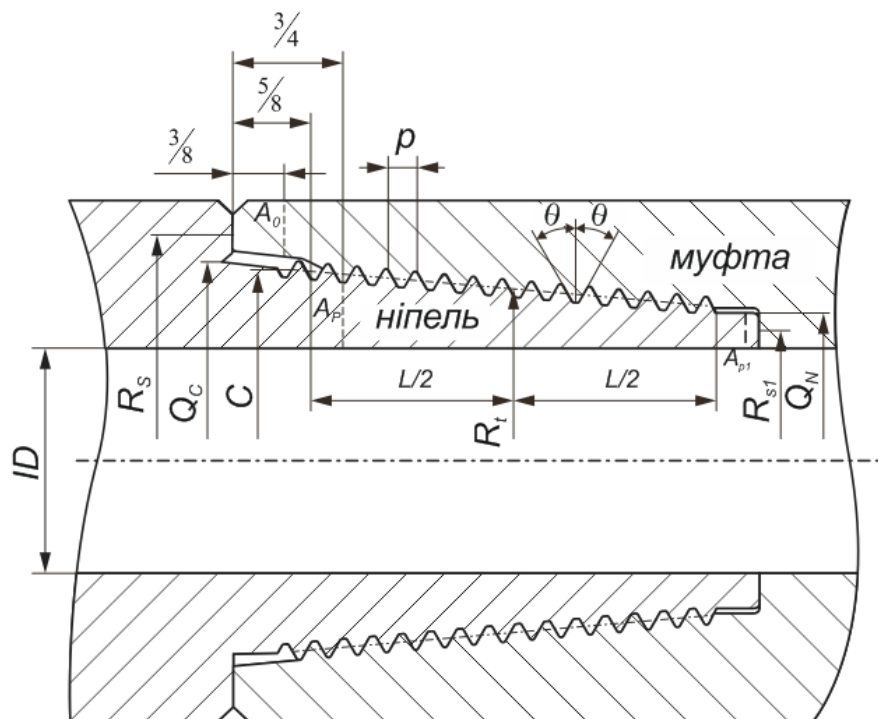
Розрахункова схема двоопорного з'єднання
